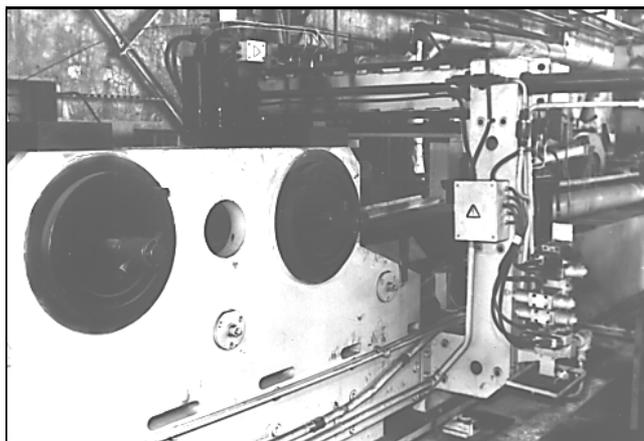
Внешний вид стана для прокатки заготовок направляющих опор пневмоподвески
